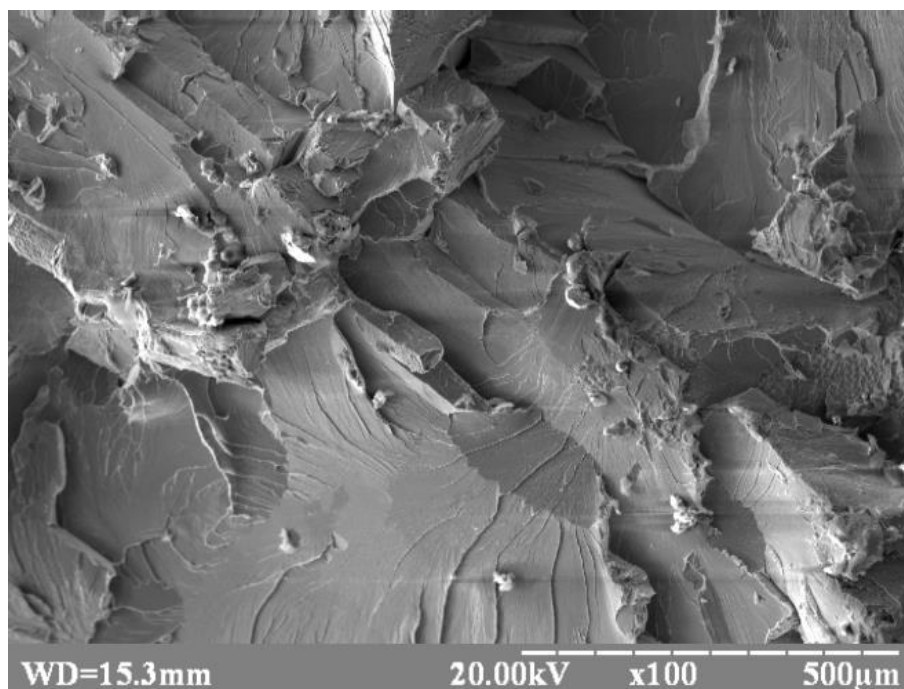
Зовнішній вигляд зварного шва з'єднання «сплав Ti-TiB»-«V»-«сталь 12X18H10T».
